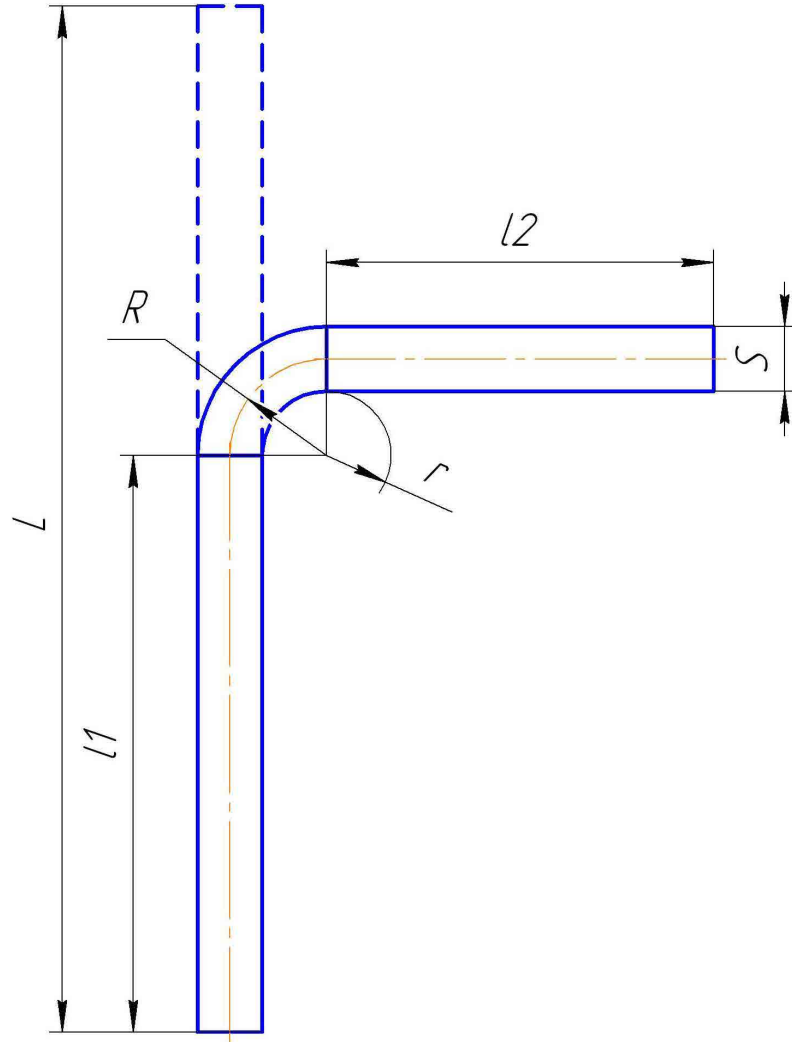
До розрахунку довжини вихідної заготовки
